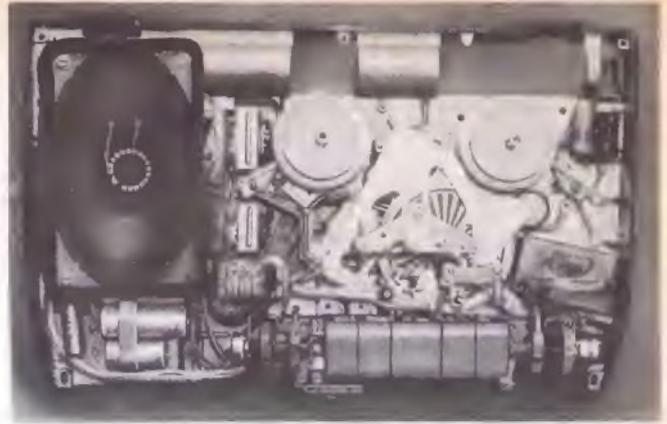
Oberseite, Frontplatte abgenommen; zum Justieren des Fliehkraftreglers am Motor befindet sich eine Stroboskopscheibe auf der Schrumngmasse
